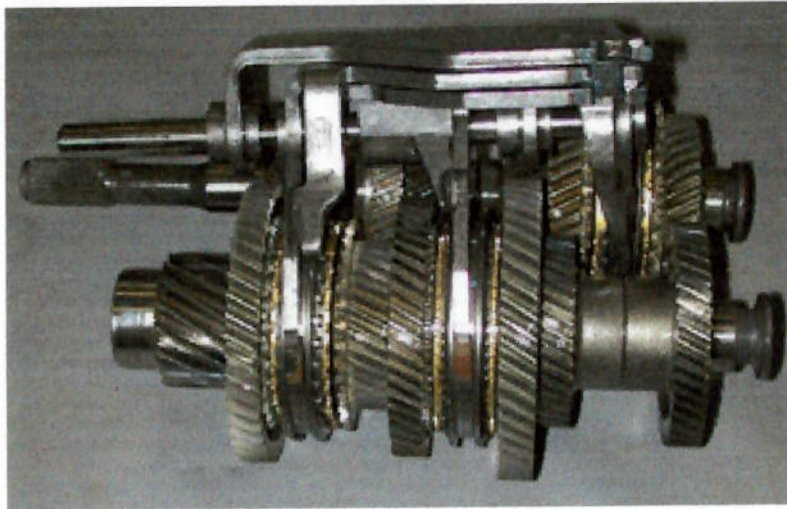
Eixo de entrada, trem de engrenagens e garfos
